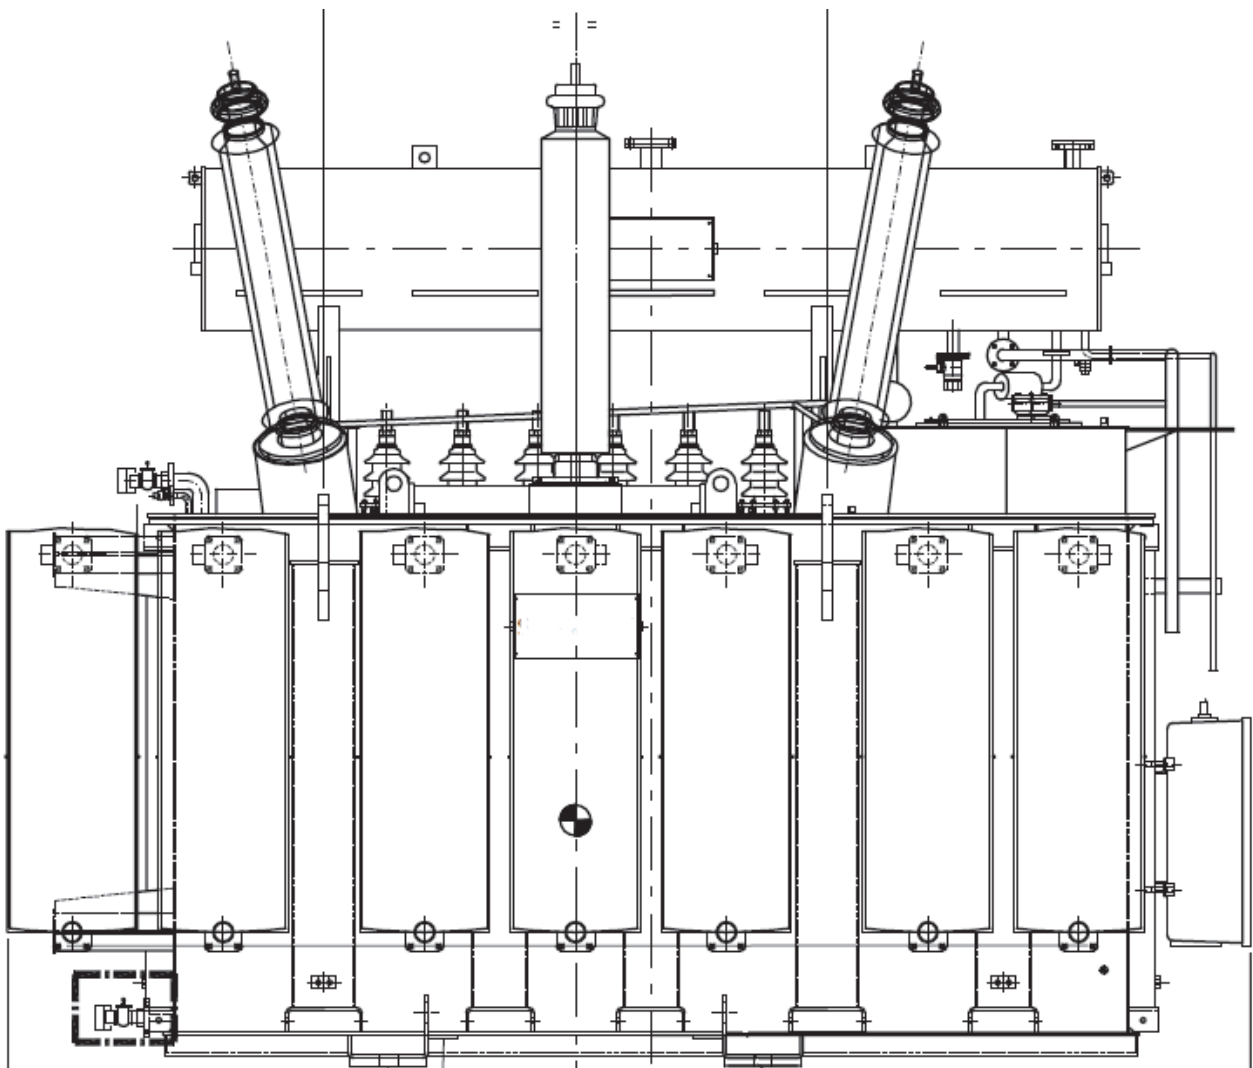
Disegno tecnico del trasformatore di gruppo.
